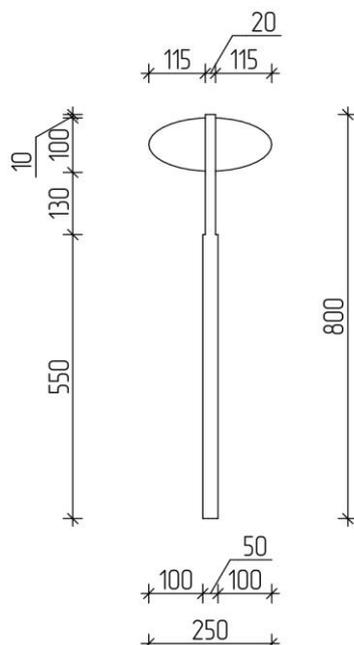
Чертеж барабана. Вид сбоку
